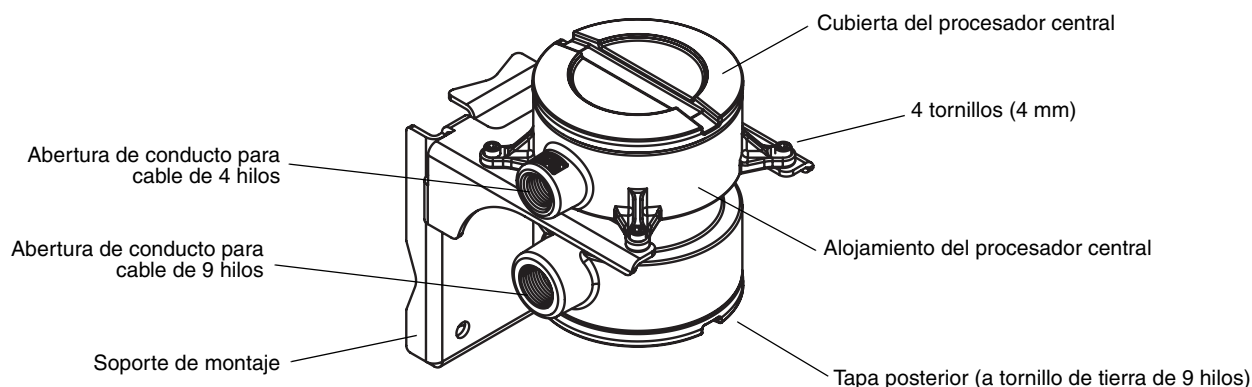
Procesador central remoto – Montaje en pared o montaje en tubo
